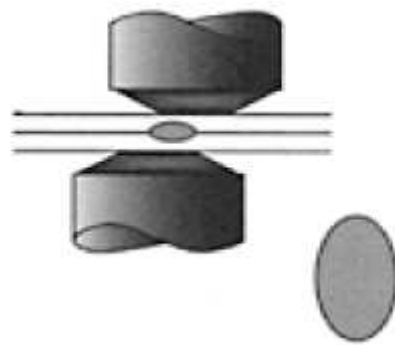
6. Punto de soldadura elíptico producido por un electrodo desalineado axialmente una distancia  $b$ .
